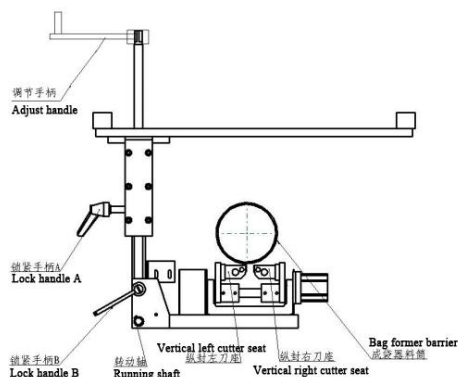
中封机构示意图 FIG. 30 schematic diagram of middle sealing mechanism
